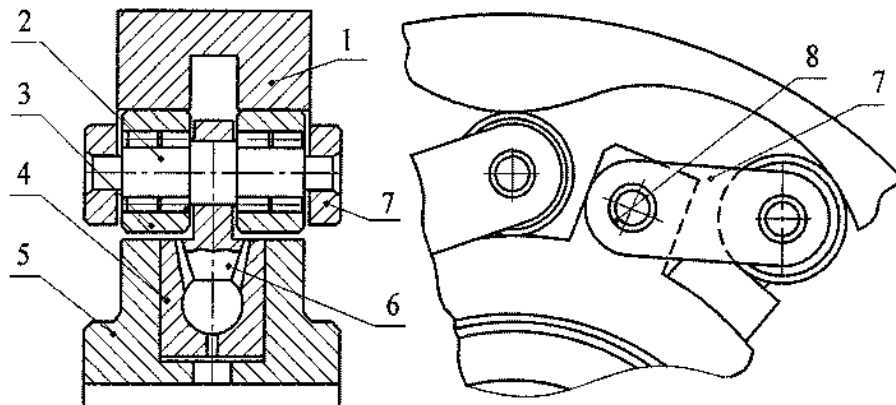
Поршневая группа гидромотора с разгрузкой поршня с помощью рычагов 7 на цапфах 8
